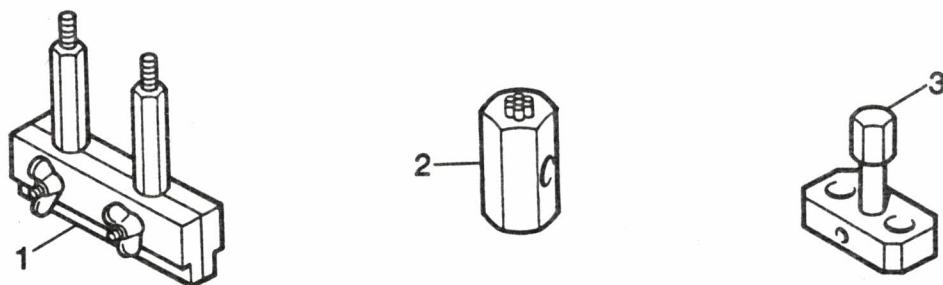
Sonderwerkzeuge, Meß- und Prüfgeräte
